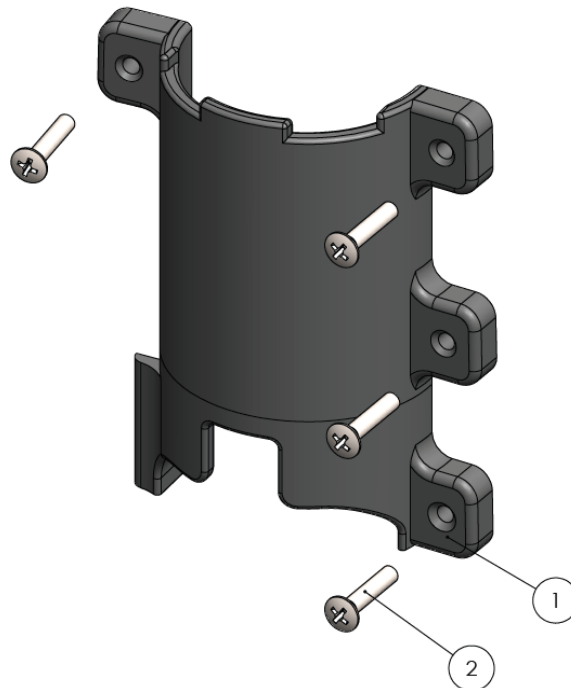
Vista explosionada del subconjunto de la Envoltura.
